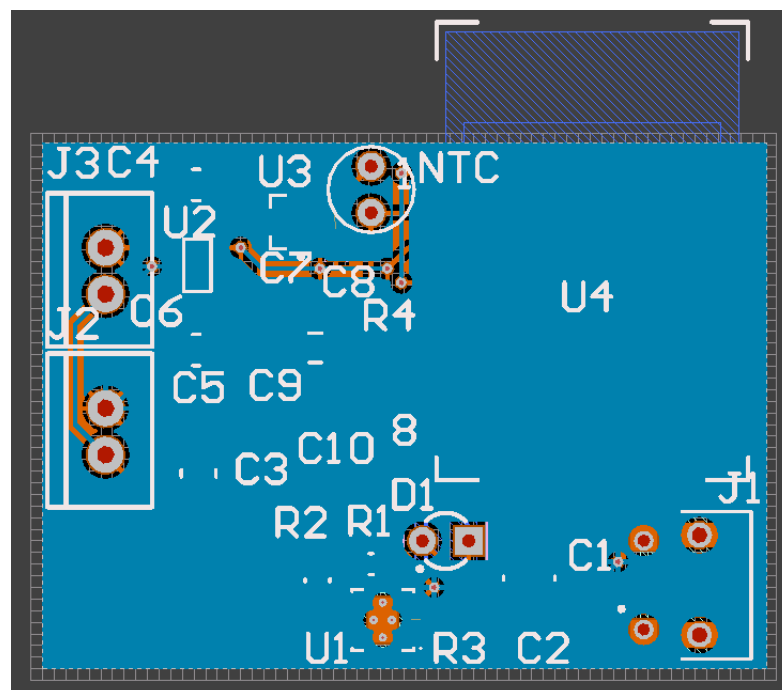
Cara inferior de la PCB diseñada con componentes SMD
